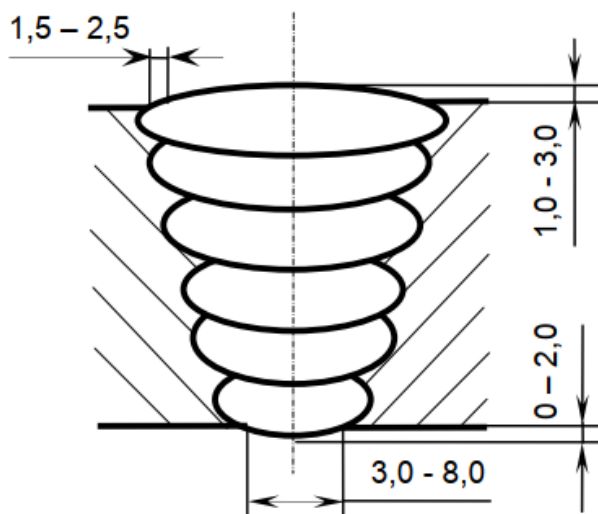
Геометрические параметры сварного шва, выполненного сварочным комплексом CWS.02
